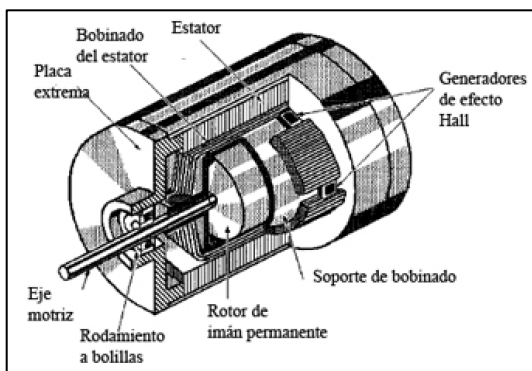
Vista en corte de un motor DC sin escobillas. [2]
